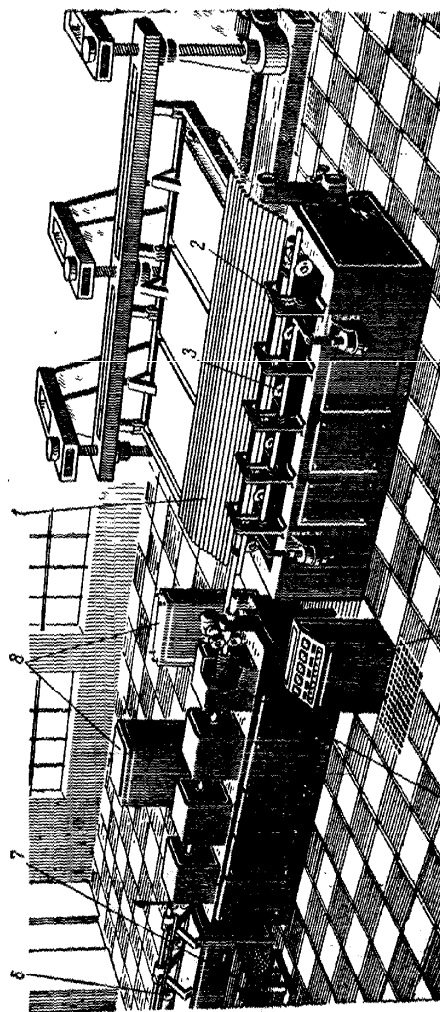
Установка для рекристаллизационного отжига стального проката: 1 — магazin для заготовок; 2 — отсекающий, пропускающий заготовки по одной на ролик; 3 — ролик, подающий заготовку в индуктор; 4 — пункт управления установкой; 5 — индуктор; 6 — наклонно вращающиеся ролики, сбрасывающие заготовки в приемное устройство; 7, 7' — приемное устройство для охлаждения заготовок; 8 — шкафы управления.
